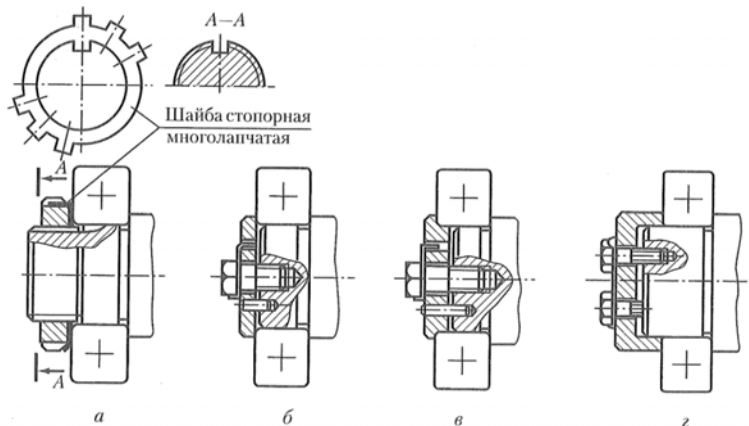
Варианты конструкций крепления внутреннего кольца подшипника к валу в плавающей опоре с помощью:
